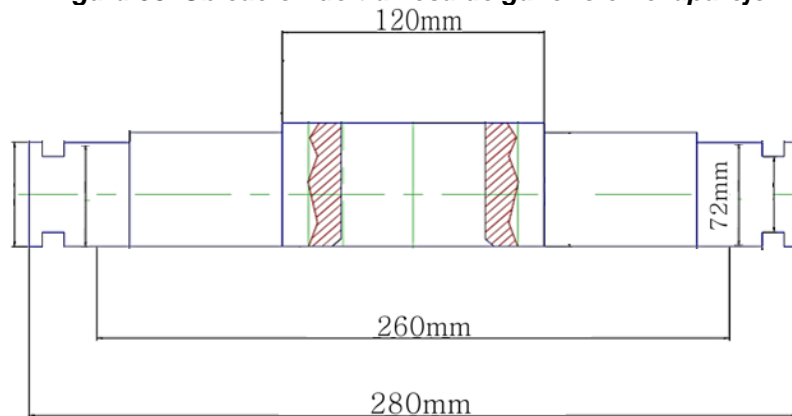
Medidas propuestas en milímetros para traviesa de gancho
